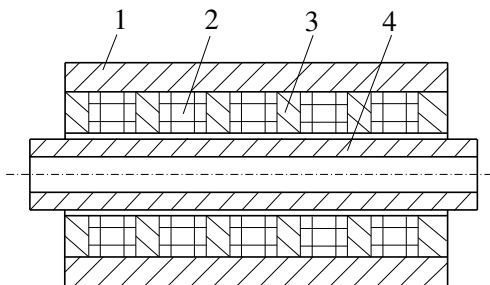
Цилиндрический (коаксиальный) линейный двигатель: 1 – индуктор двигателя; 2 – обмотки индуктора; 3 – металлические шайбы; 4 – вторичный элемент
